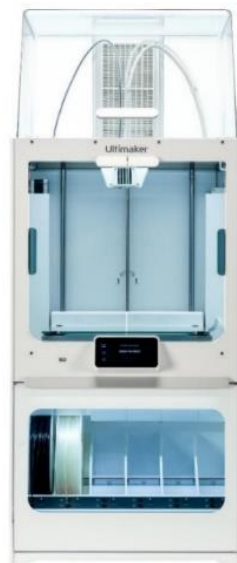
Impresora 3D Ultimaker S5 || Fuente: [farnell.com](https://www.farnell.com)
